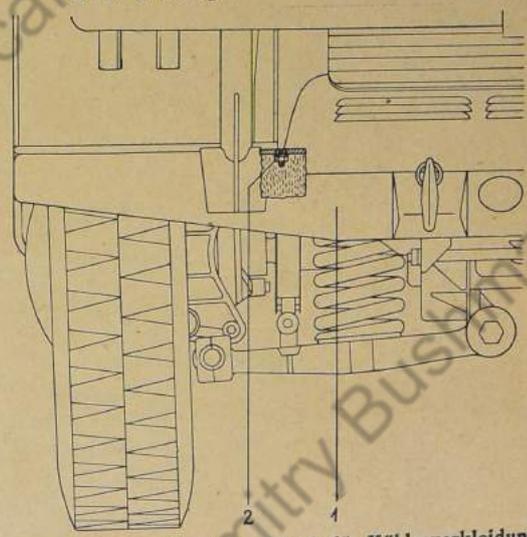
Befestigung des Bügels für Kühlerverkleidung am 1. Querträger
